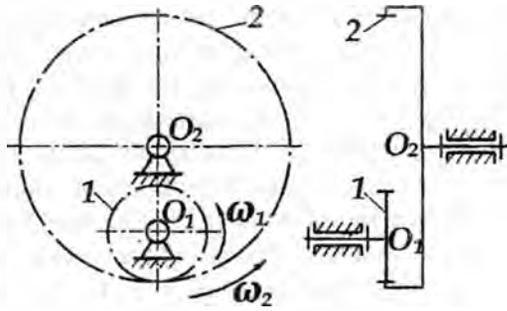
Вид и схемы цилиндрических зубчатых передач:
